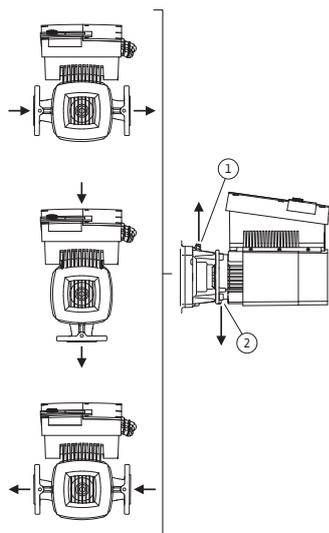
Posiciones de montaje admisibles con eje del motor horizontal
